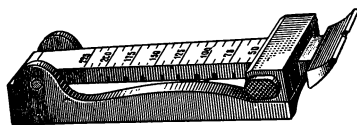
Секторный открытый прицел спортивной малокалиберной винтовки, модель ТОЗ-8
